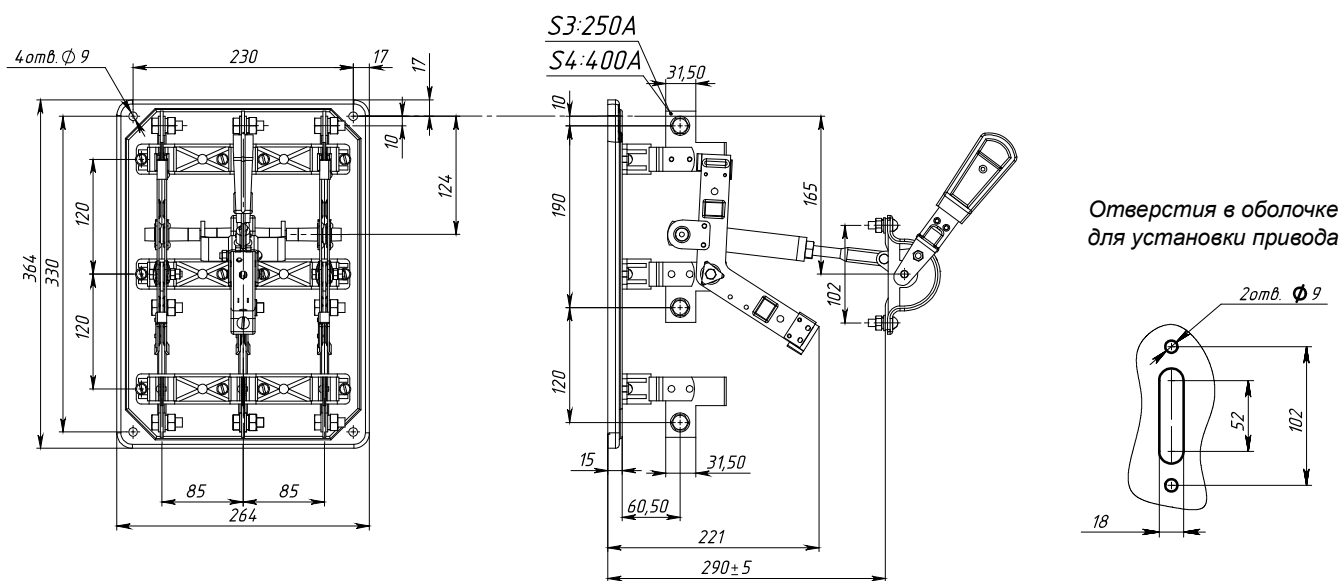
Разъединитель типа ПЦ с центральным приводом на токи 250 А и 400 А
